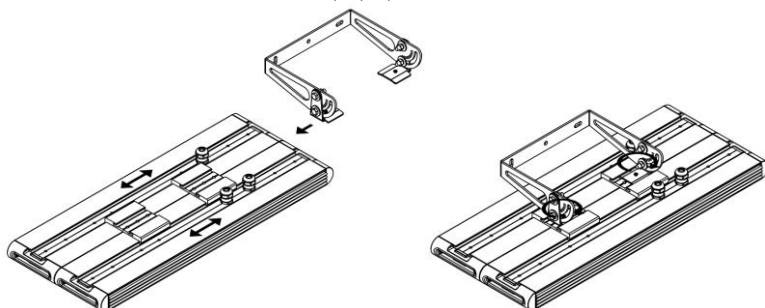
Установка крепления на соединительные планки на примере светильника Element 0,5x2 и Крепления Скоба малая с регулировкой.
